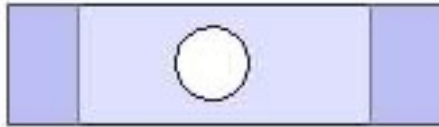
Onder- en bovenaanzicht bovenste strook
